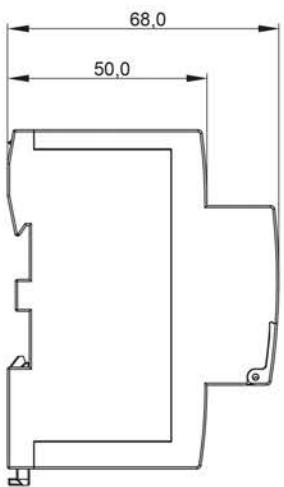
Габаритные размеры контакторов 100 А, 4Р / Figure 6 – Overall dimensions of 100 A, 4P contactors
